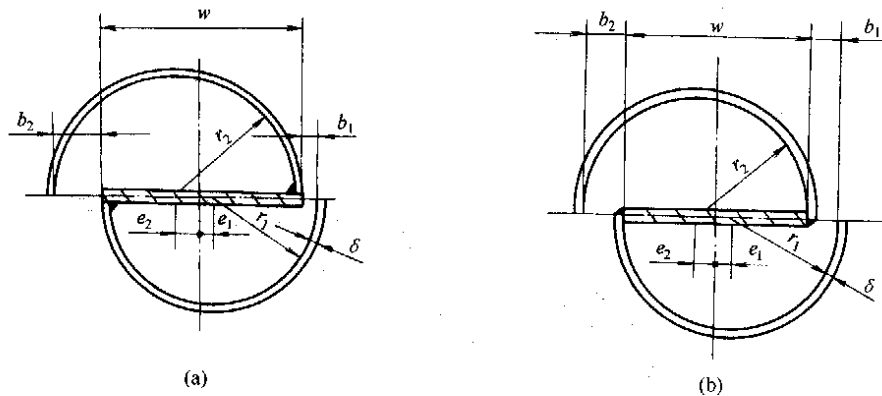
中心隔板与螺旋板的焊接结构
